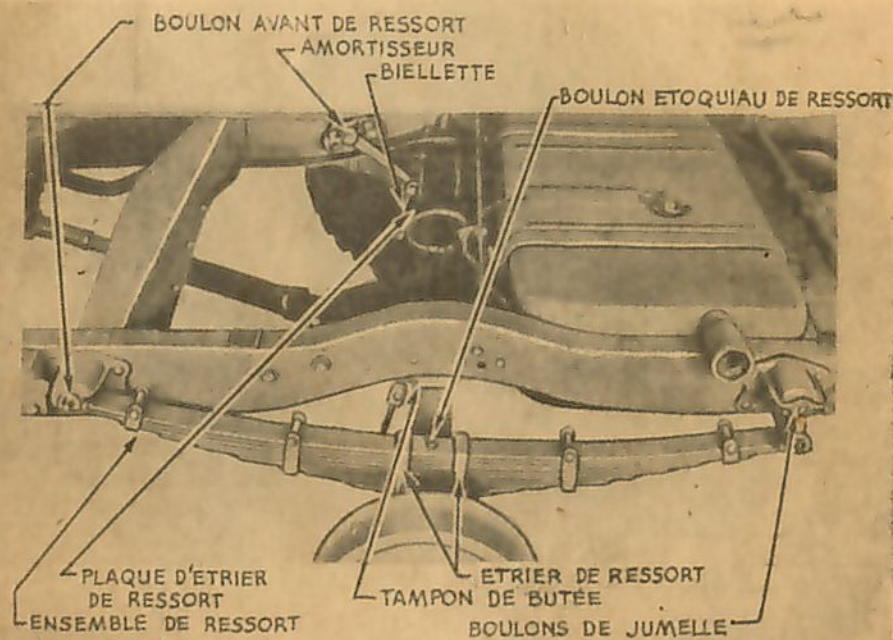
Vue de la suspension arrière sur châssis 3/4 T. 4 x 4.
